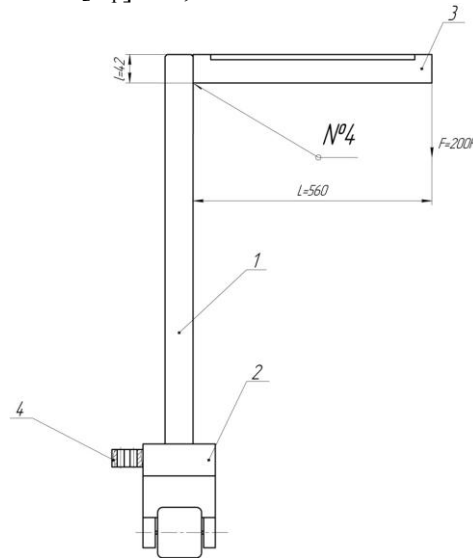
Стойка станда для разборки – сборки коробок передач:
